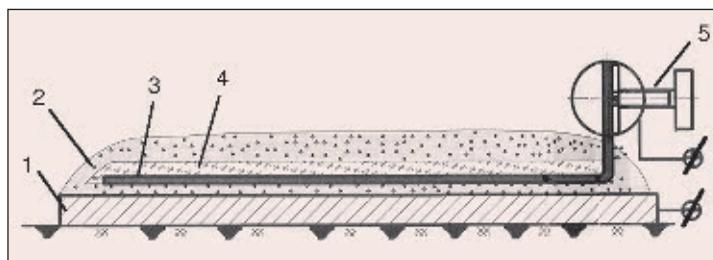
Схема электродуговой наплавки неподвижным плавящимся электродом под флюсом с порошком: 1 — наплавляемая деталь; 2 — флюс; 3 — составной электрод; 4 — ППМ; 5 — электрододержатель
